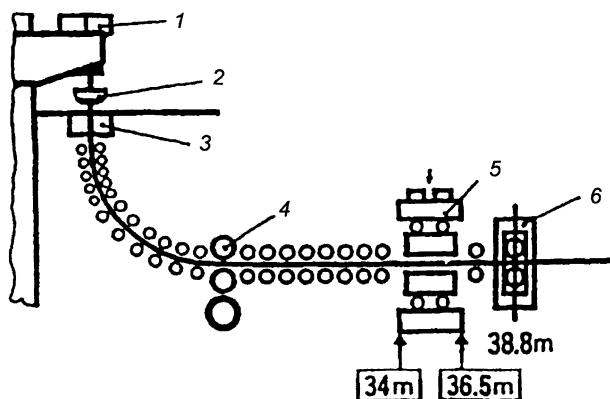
Схема расположения оборудования при использовании «мягкого обжата» сляба: 1 – стелеразливочный ковш; 2 – промковш; 3 – кристаллизатор; 4 – точка разгиба сляба; 5 – зона обжата; 6 – тянущая клеть
